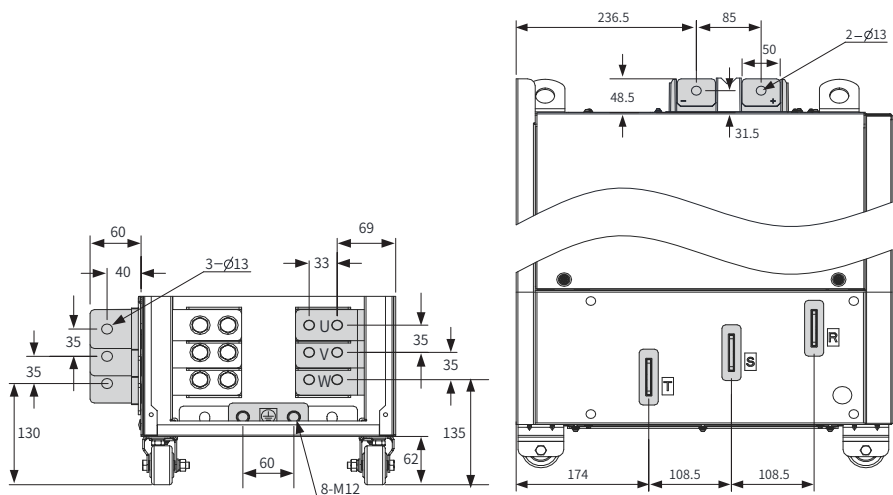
Размеры клемм главной цепи MD880-01S-0441-4/MD880-01S-0481-4 (без выходных реакторов)
